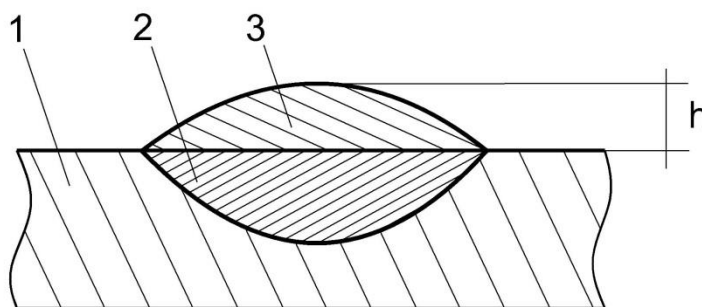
Сечение наплавленного валика: 1 - основной металл, 2 - площадь сечения расплавленного основного металла F_o , 3 - площадь сечения наплавленного металла F_n , h – толщина наплавленного слоя
